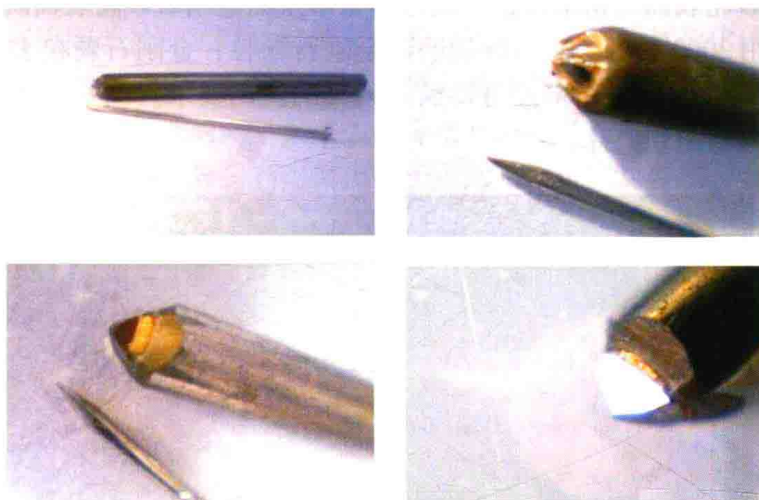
焊接刀杆式圆柱立铣刀毛胚
